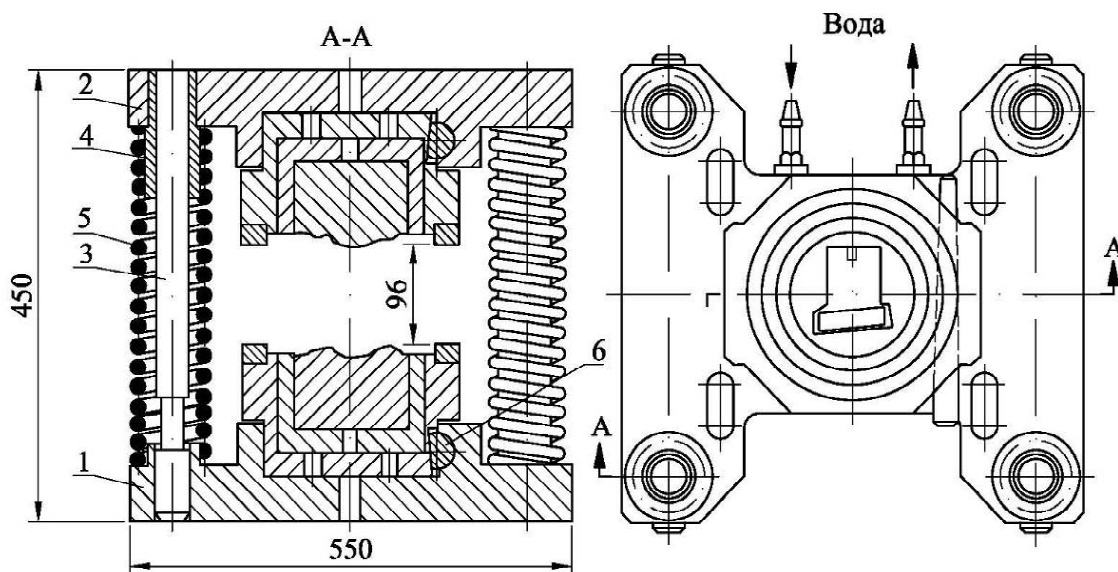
Штамповый блок: 1, 2 – нижняя и верхняя плиты; 3 – направляющая колонка; 4 – втулка; 5 – пружина; 6 – клин. Отверстия для водяного охлаждения плит не показаны
